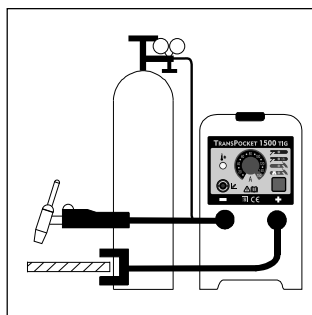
TP 1500 equipado para soldadura TIG
